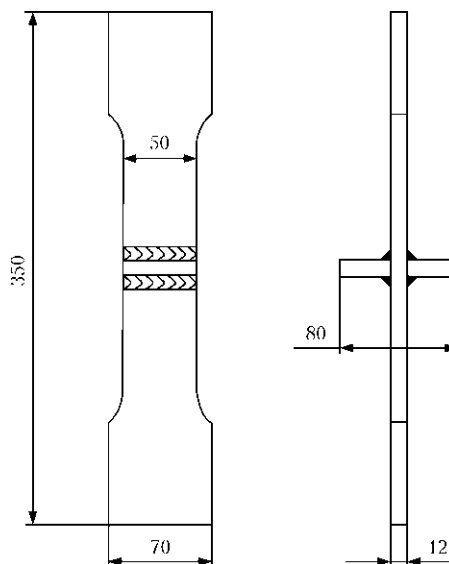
Форма и размеры образца таврового соединения стали 09Г2С
